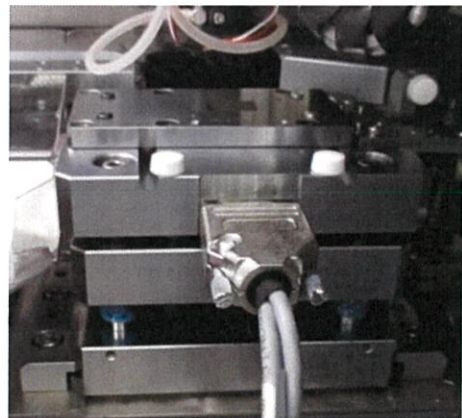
(ข) แสดงเครื่องมือ Cutting Tool B
